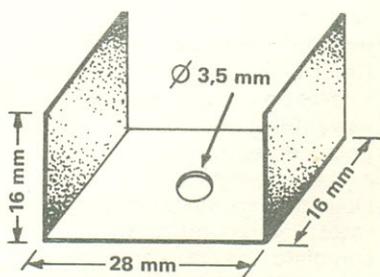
Desenho e dimensões do dissipador do transistor de potência. Utilizar chapa de alumínio de (pelo menos) 2 mm de espessura.
